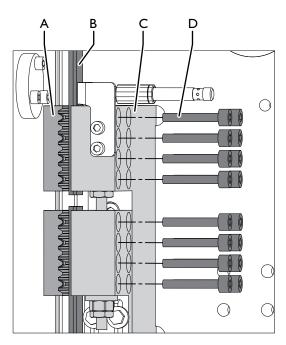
Riemenbefestigung entfernen: 2.Stufe, fix, rechts
